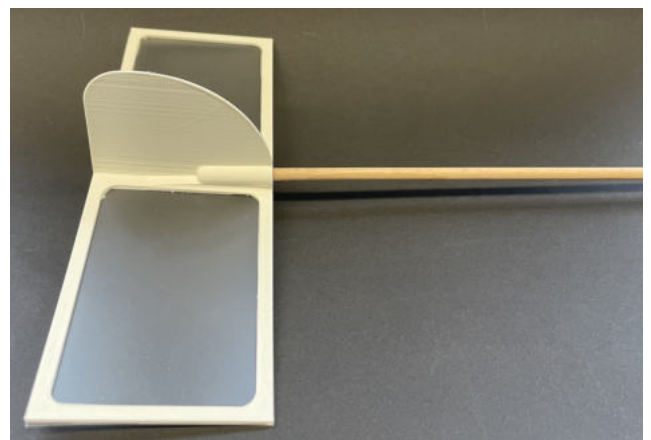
Das Leitwerk wird mit dem 5mm Rundholz verbunden.
